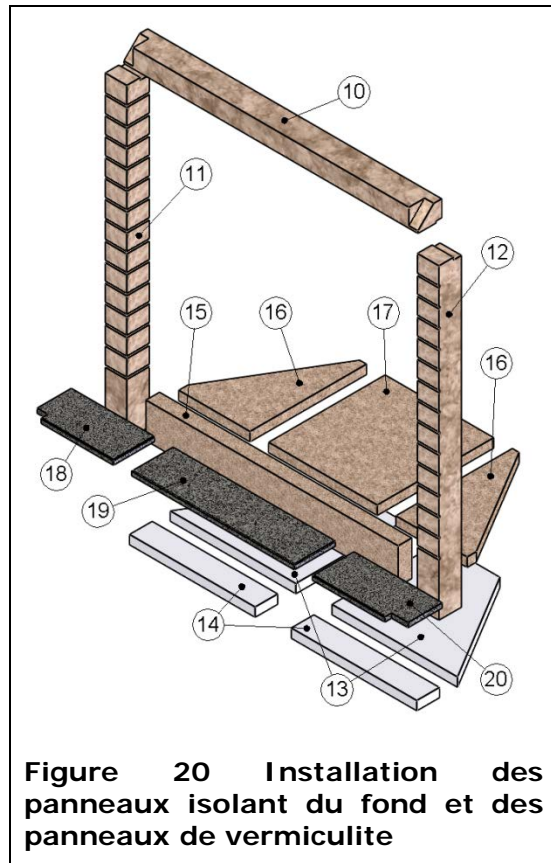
Installation des panneaux isolant du fond et des panneaux de vermiculite
